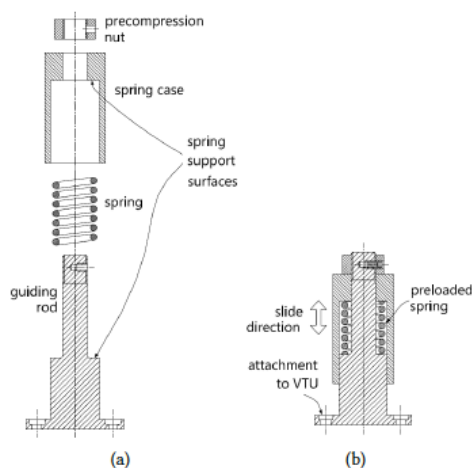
Representació esquemàtica de la unitat de regulació de la força: a) Vista explosionada; b) Parts acoblades i compressió del motlle (24).
